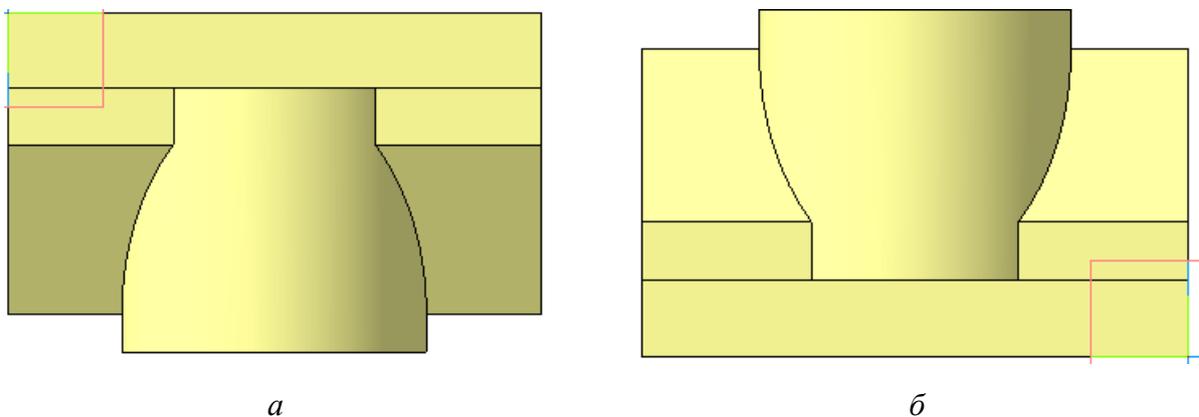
Поворот корпуса в удобное для *Главного вида* положение
